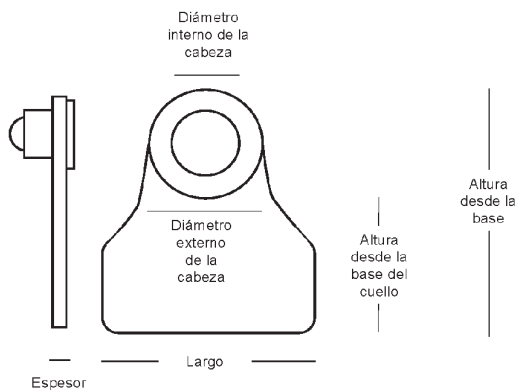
Detalle de crotal tipo bandera - pieza hembra
